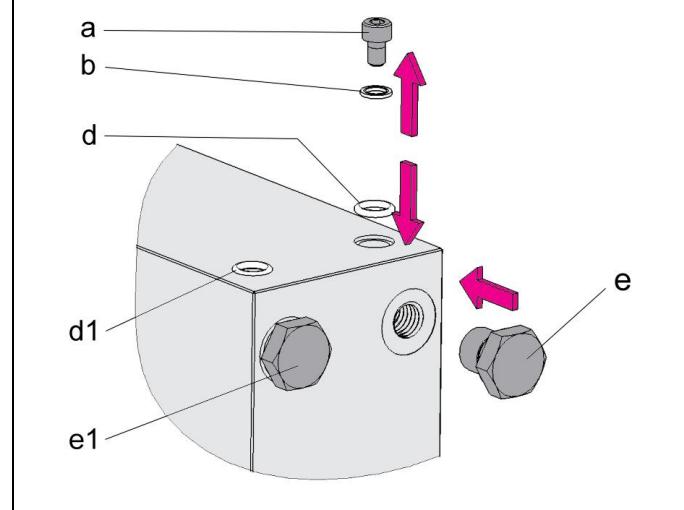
Esempio, installazione della versione a flangia (senza tubi)
